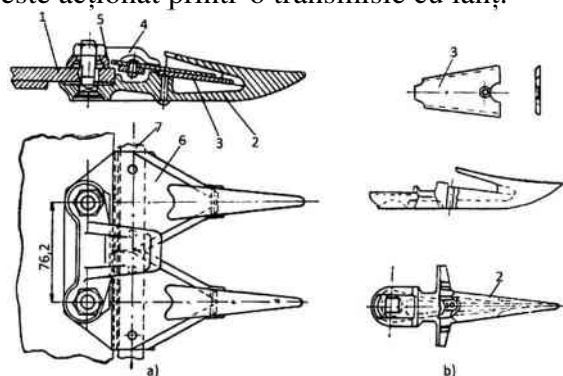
Aparat de tăiere: a – părți componente; b – degetul cu placa contrațaietoare
